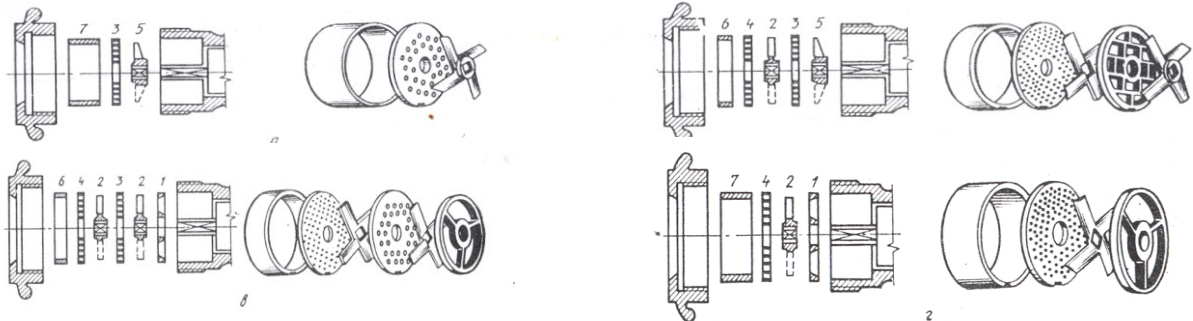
Схема зборки подрібнювальних механізмів вовчків:
